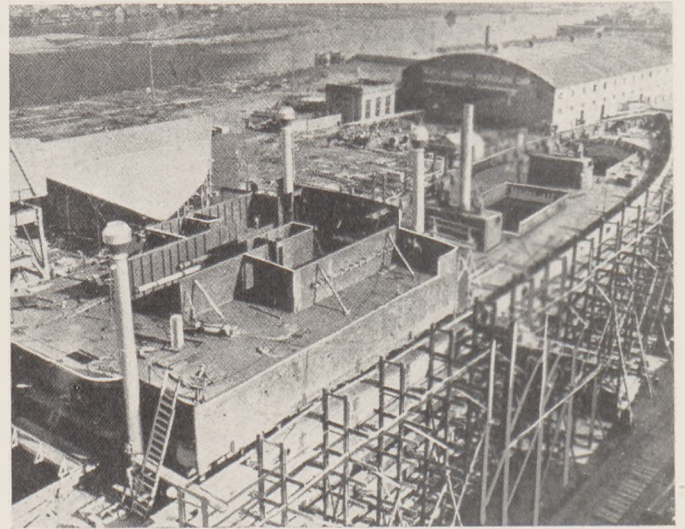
Vorfabrizierte Decksaufbauten werden aufgestellt.
